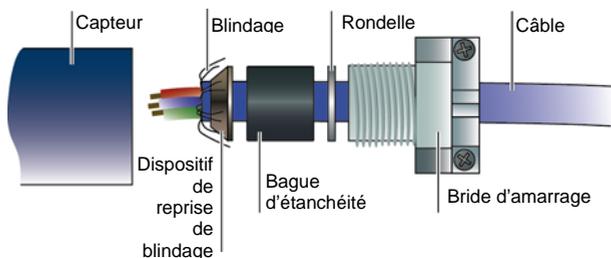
exemple de presse étoupe simple compression pour serrage sur câble souple.
